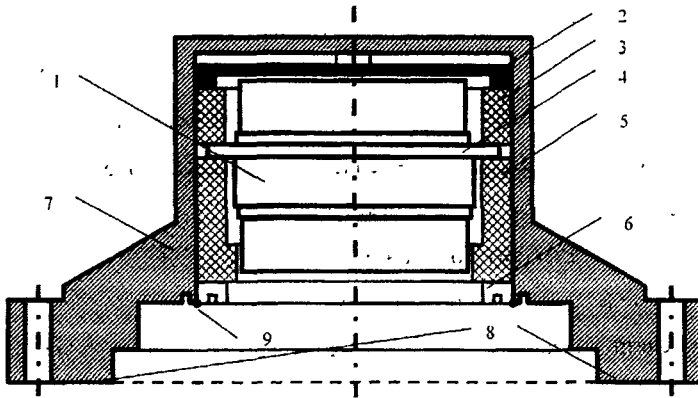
Крепление ЧЭ в корпусе АК-6. 1. Чувствительный элемент (ЧЭ), 2. Плоская пружина, 3, 5. Втулки (керамика), 4. Фланец соединительного кольца, 6. Запорная шайба, 7. Корпус АК-6, 8. Базовая (установочная) плоскость корпуса, 9. Точечная лазерная сварка
